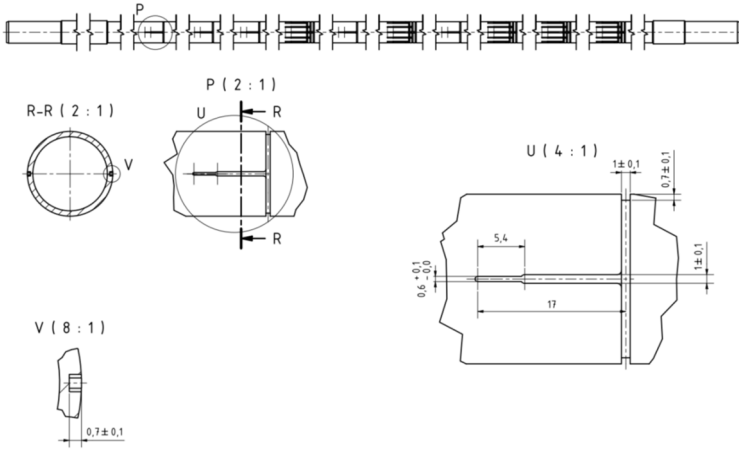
Technische Zeichnung des Messrohres aus Alloy 201 mit Nutbild und Positionierung der Thermoelemente für Messebenen mit zwei Thermoelementen.
